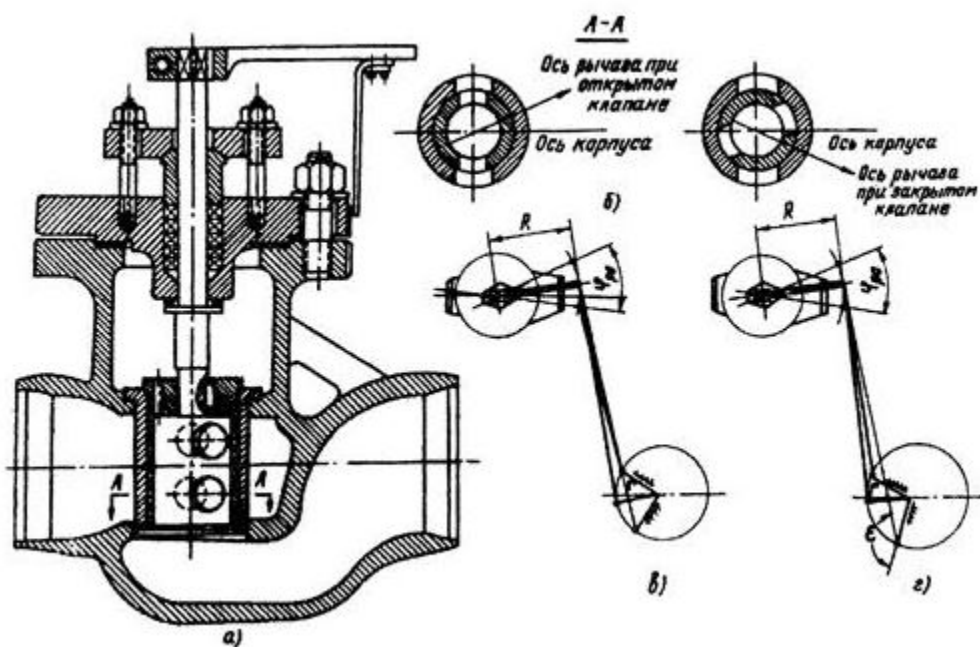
Однопоточный поворотно-золотниковый клапан:
